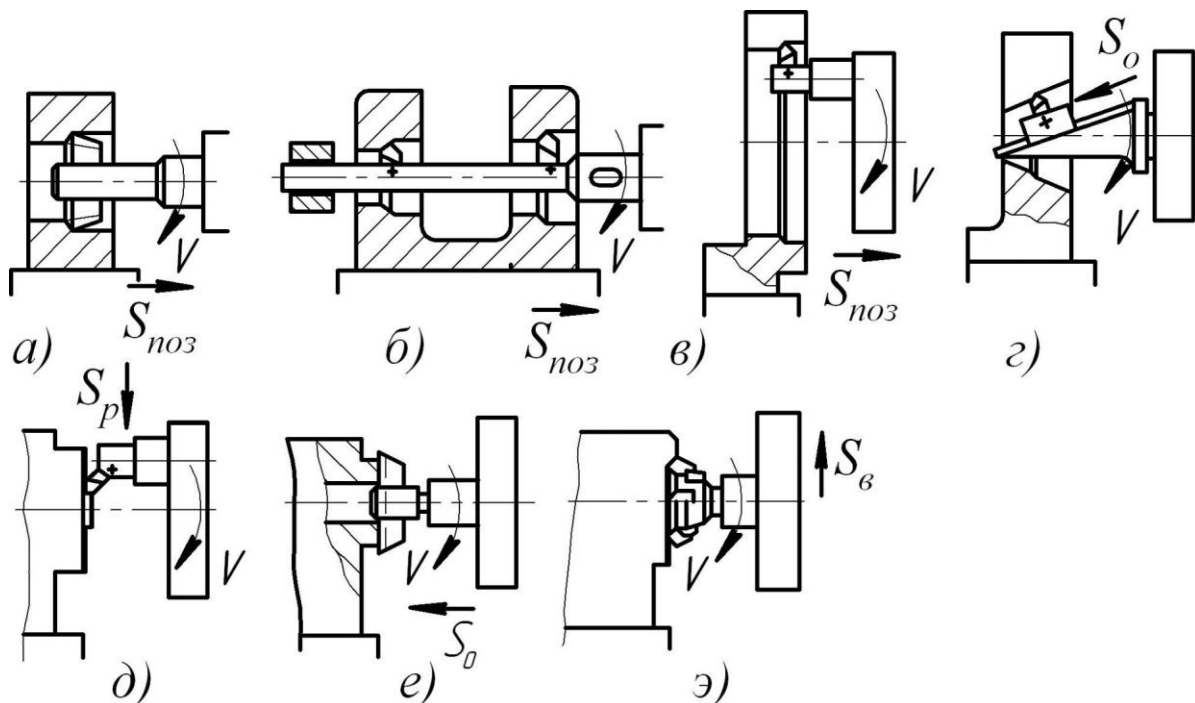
Схеми обробки заготовок на горизонтально-розточувальних верстатах
